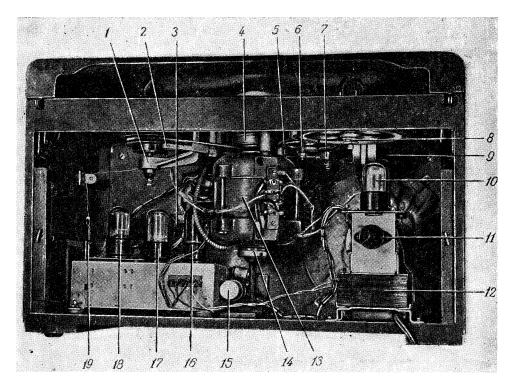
Расположение деталей лентопротяжного механизма и усилителя.
